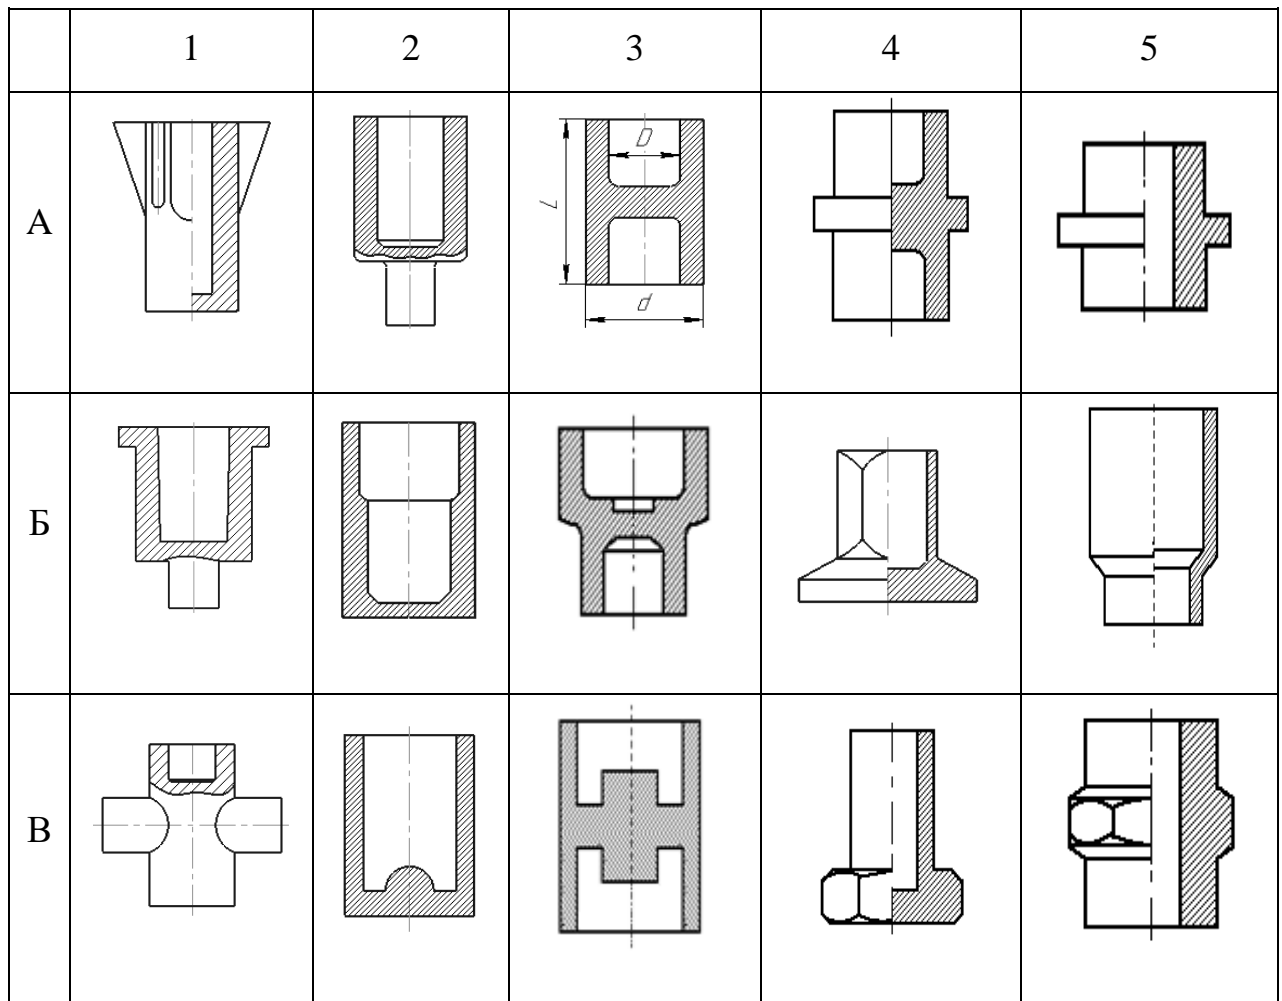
Типи порожнистих деталей, які виготовляють ХОШ
